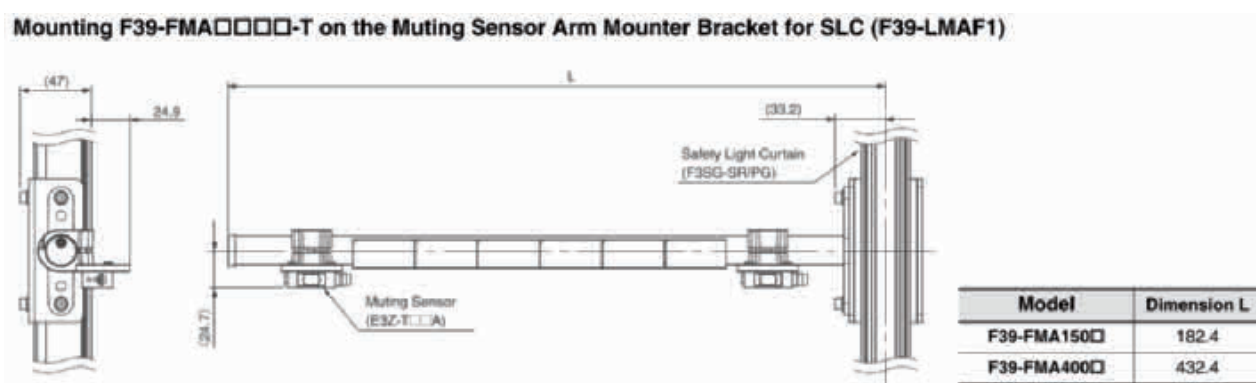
Fissaggio braccetti di muting sulla barriera con staffa F39-LMAF1
